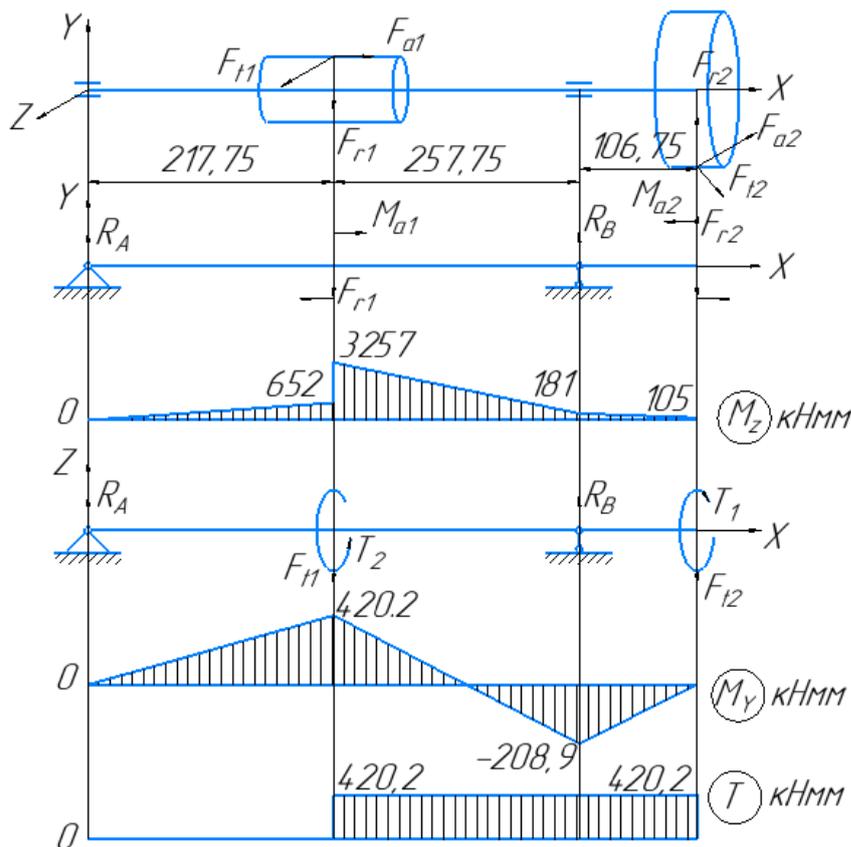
Розрахункові схеми проміжного валу редуктора
